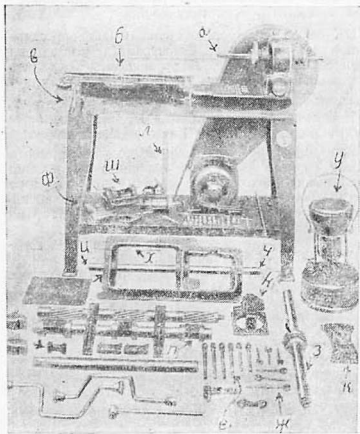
Станок с приспособлениями и инструментами для расточки цилиндров, заливки, расточки и развертки коренных подшипников двигателей «Форд»
